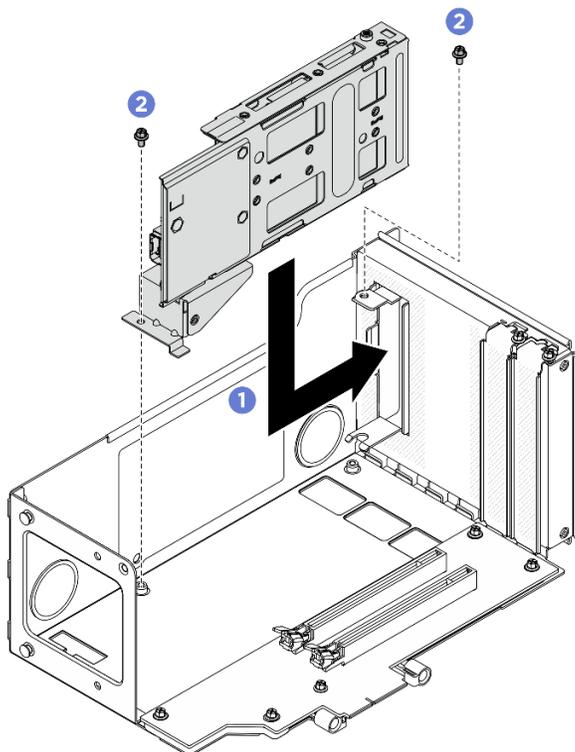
Installation du boîtier d'unités M.2 sur la carte mezzanine
